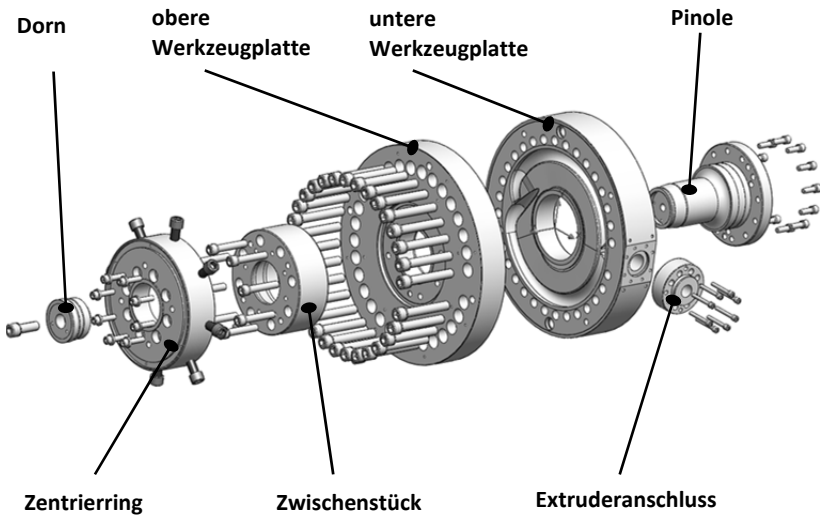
Explosionsansicht des Versuchswerkzeuges
